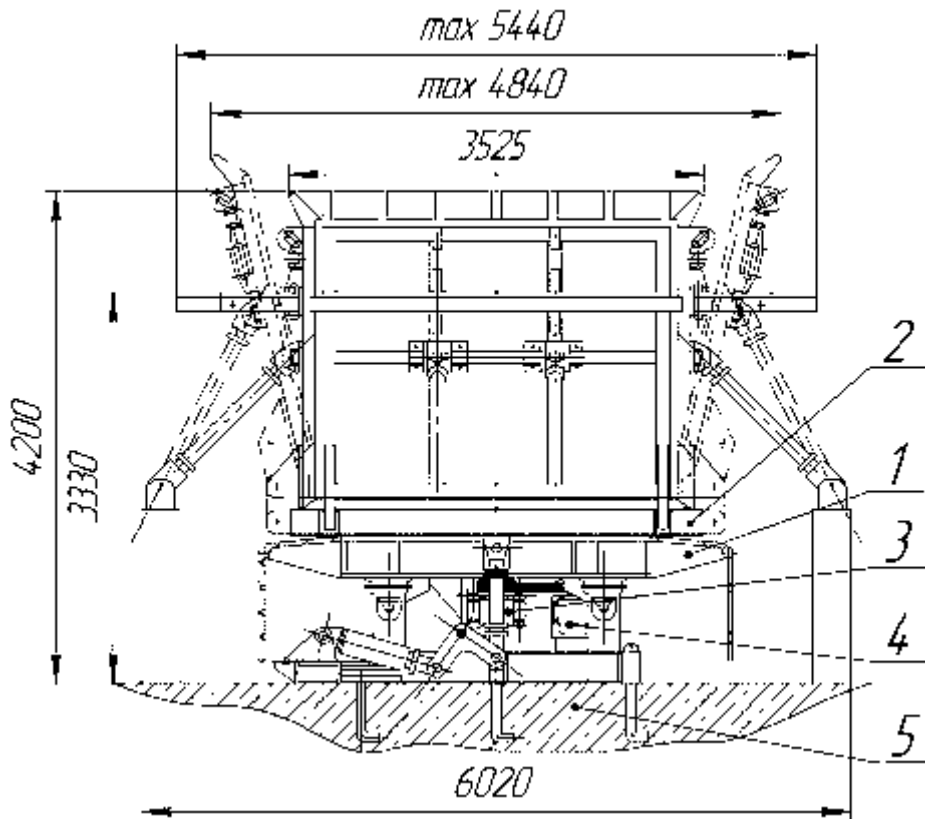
Схема віброустановки ВПСЛ-2х2,9 для формування бетонних об'ємних блоків шахт ліфтів: 1 – рухома рама; 2 – форма; 3 – віброзбуджувач; 4 – електродвигун; 5 – фундамент
